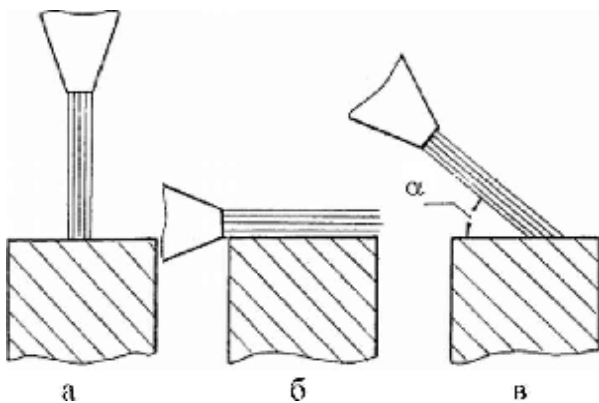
Схеми дії абразивного струменя на поверхню.
